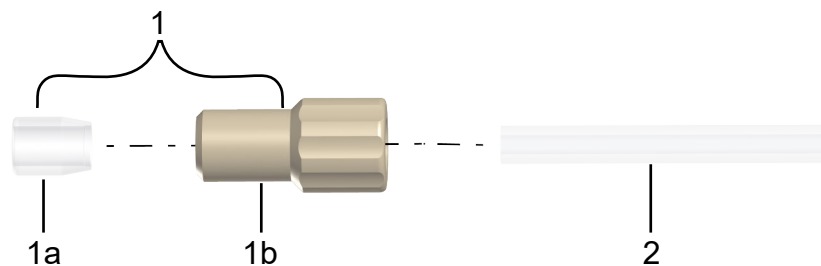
Schlauchverbindung mit flanschlos-Verschraubung
